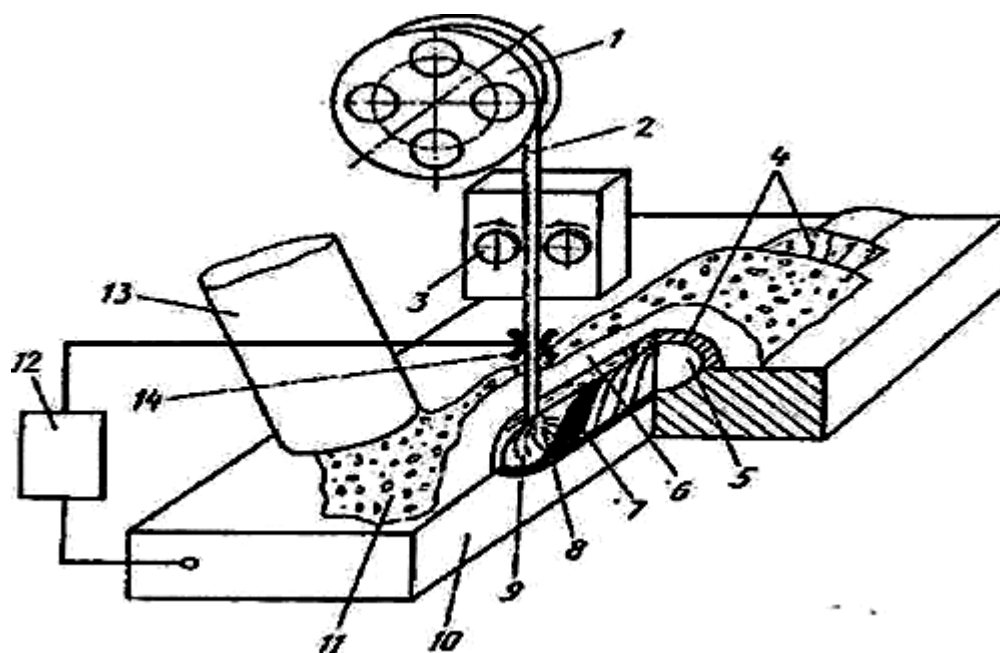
Схема процесса автоматической дуговой сварки под флюсом:
